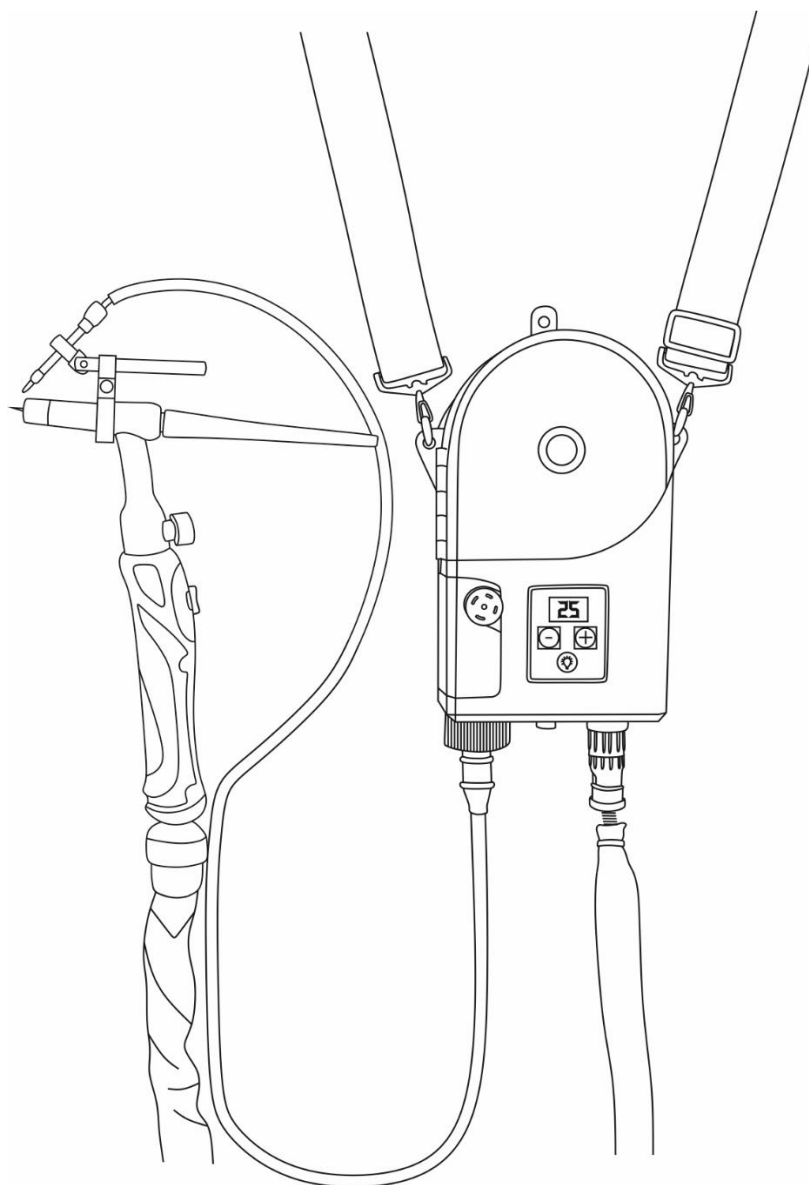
Внешний вид ППУ с подключенным рукавом и кронштейном крепления к сварочной головке устройства внешней подачи присадочной проволоки.
